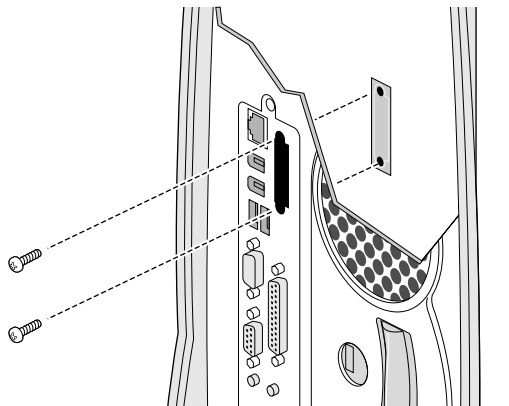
Installation de la plaque de protection sur l'emplacement de la carte d'extension graphique
